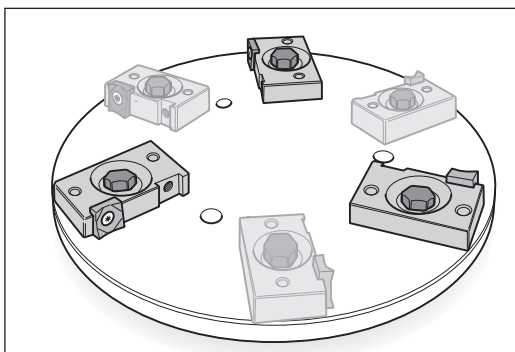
Ein Frästeller kann mit 3 oder mit 6 Plattenhaltern bestückt werden.
